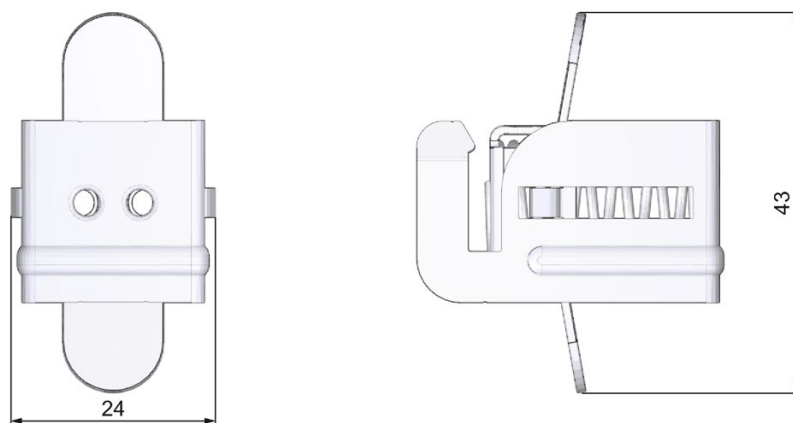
Maßbild Schirmklemme für 35 mm-Module
